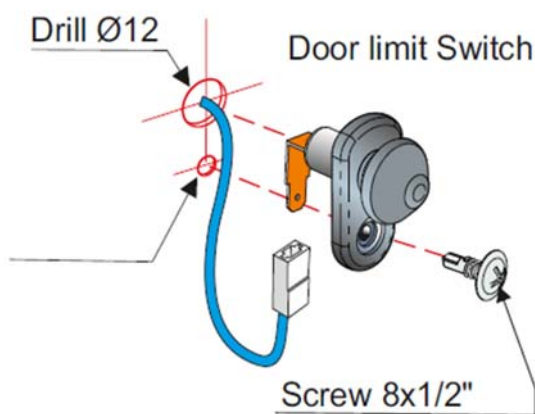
Ansicht Türkontaktschalter Aufbauschema
